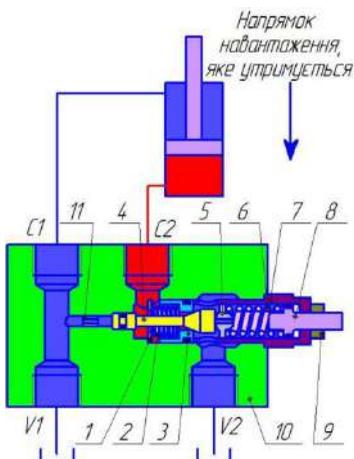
Односторонній гальмівний клапан у стані утримання навантаження: 1 – опорна шайба; 2, 6 – пружини; 3 – сідло; 4 – клапан; 5 – упор; 7 – обойма; 8 – регулювальний гвинт; 9 – контргайка; 10 – корпус; 11 – дросель
